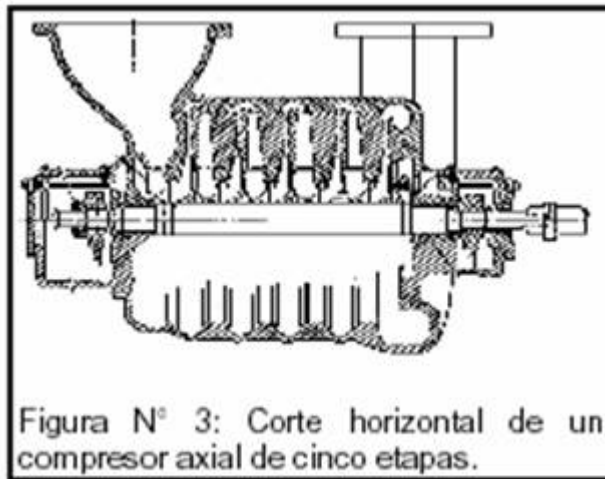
Corte horizontal de un compresor axial de cinco etapas.
